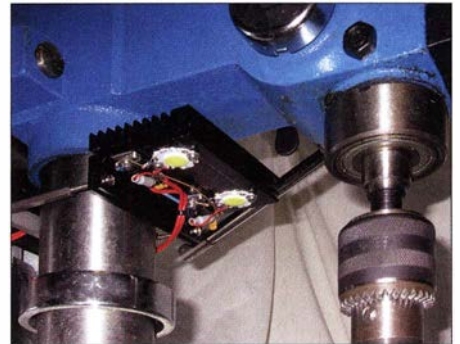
Der Kühlkörper mit der darauf angebrachten Schaltung wurde direkt mit einer selbst gebauten Klemme an der Säule der Ständerbohrmaschine befestigt.
